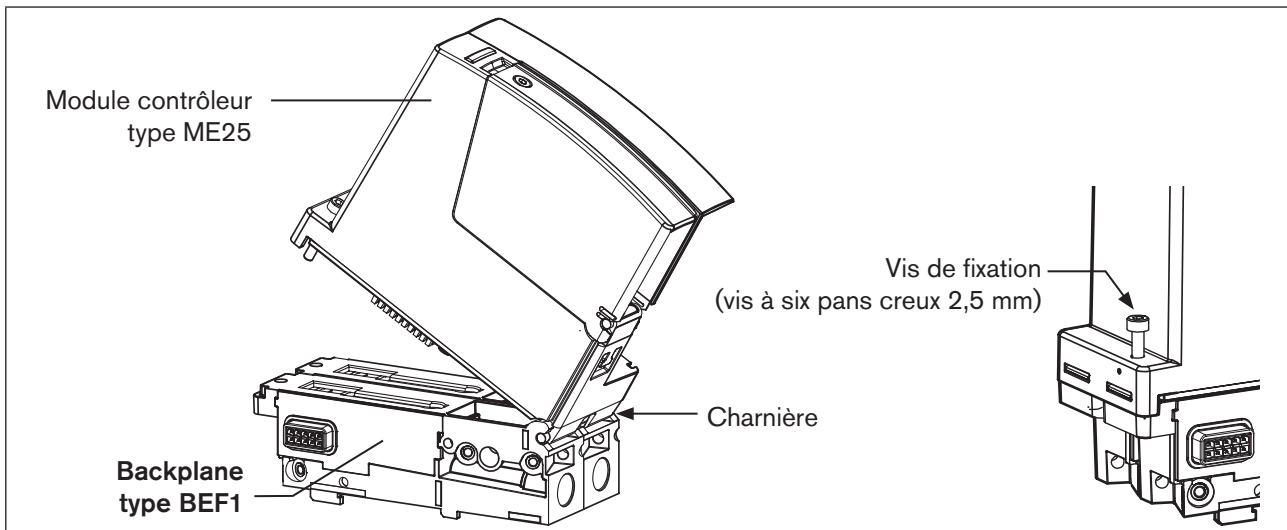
Monter le module contrôleur de type ME25 sur le Backplane de type BEF1
